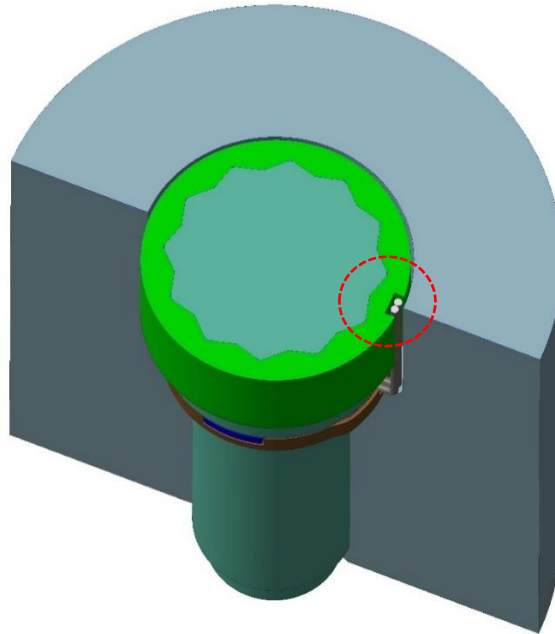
Visione assieme durante montaggio/smontaggio candela
